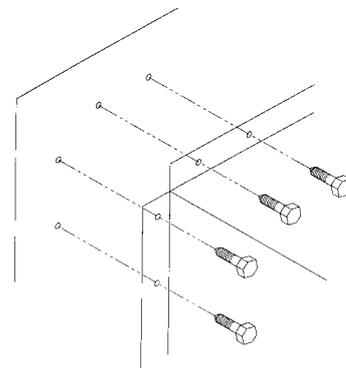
Detailzeichnung Einbau der seitlichen Ansaug-Schalldämpferhauben
